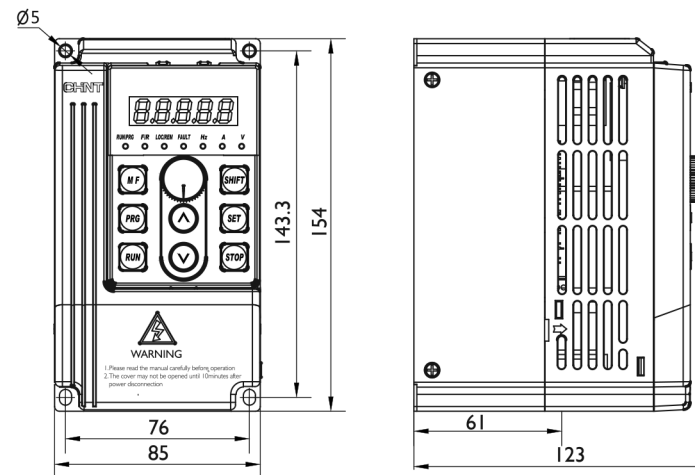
Схематический чертеж инвертора серии NVF300M
